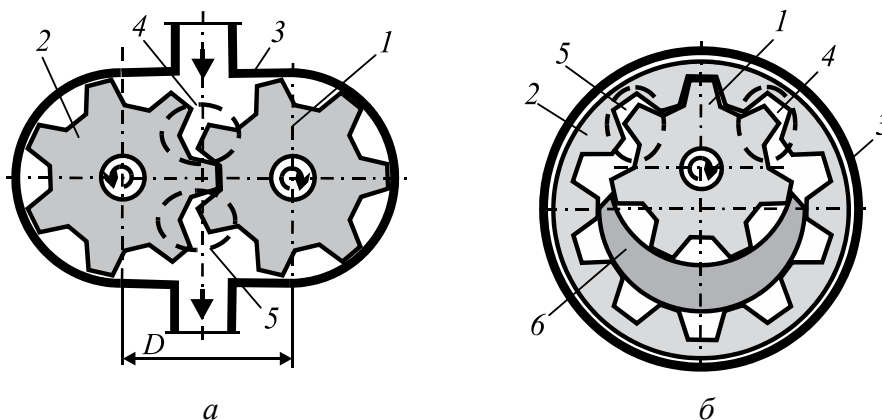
Шестеренный насос с внешним (*a*) и внутренним (*б*) зацеплением:
